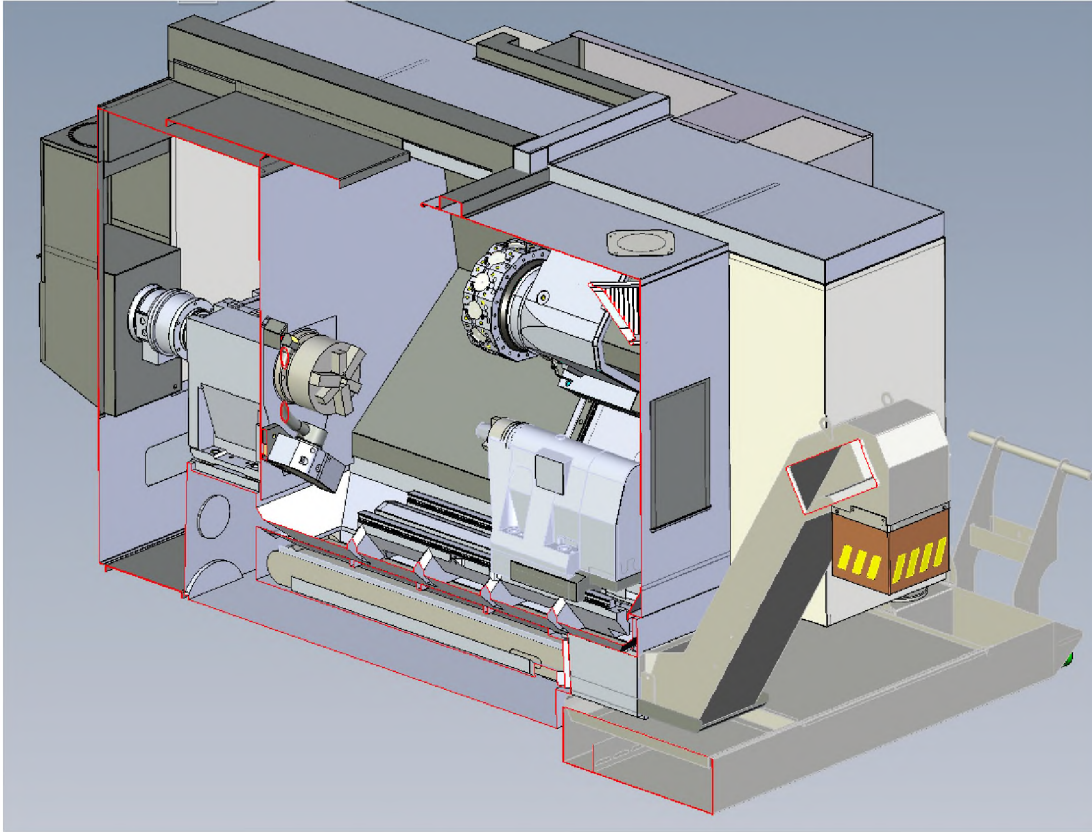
3D модель токарного центру з ЧПК HAAS ST 20 (2)
